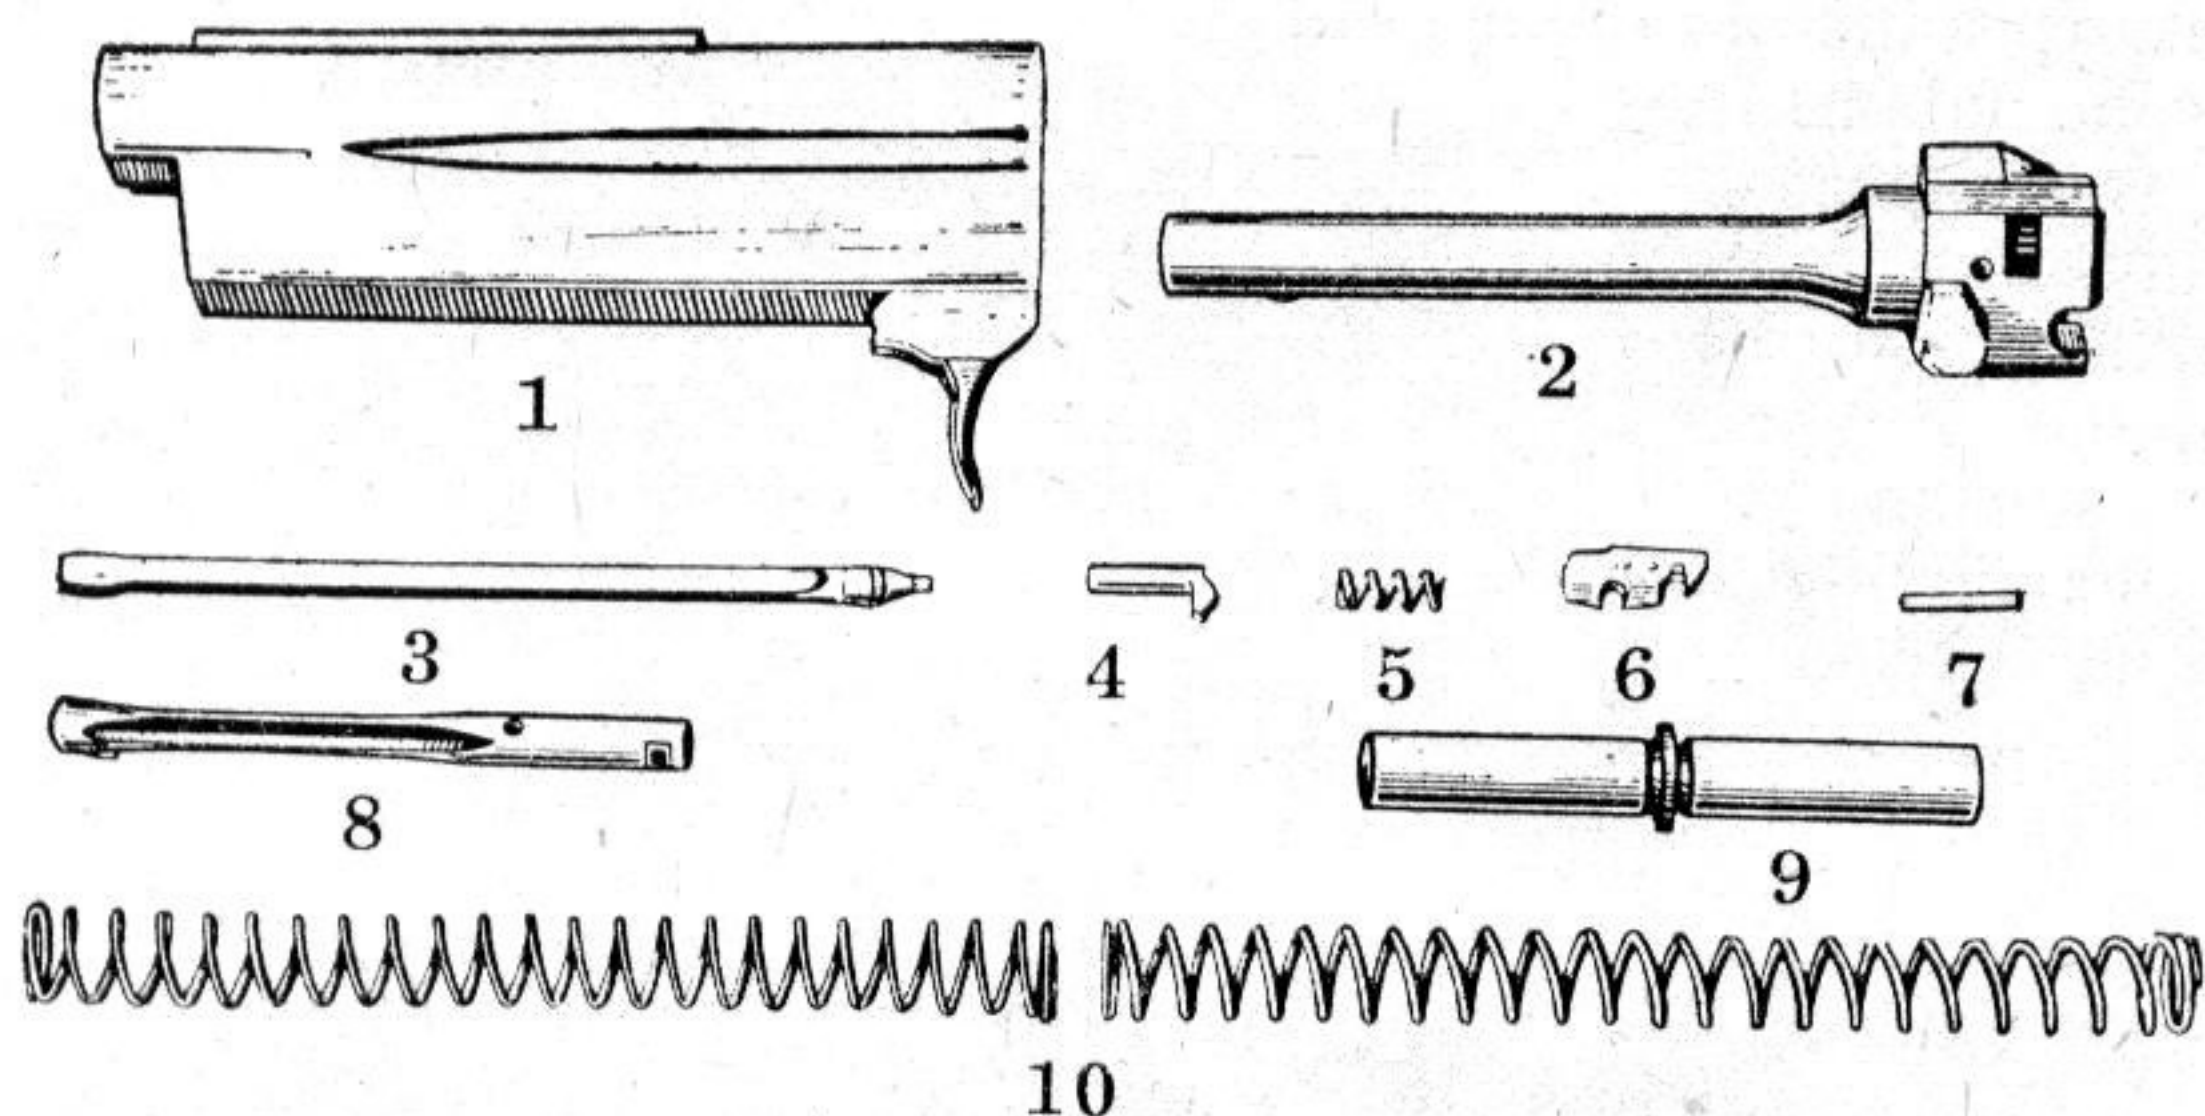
Детали затвора и возвратного механизма карабина «Медведь»:
